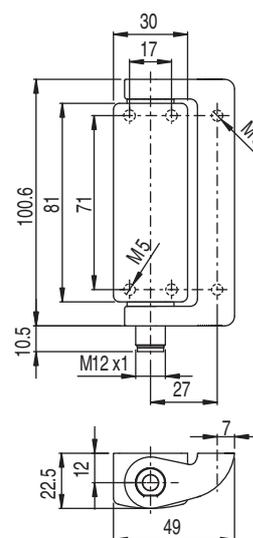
Dimensões do S400-M4M12-B em mm
